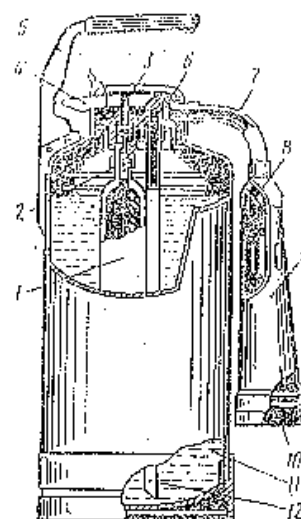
Огнетушитель химически-пенный ОХП-10 (1 - корпус; 2 - кислотный стакан; 3 - боковая ручка; 4 - горловина; 5 - рукоятка; 6 - шток; 7 - крышка; 8 - клапан; 9 - предохранитель; 10 - спрыск; 11 - нижняя ручка)
